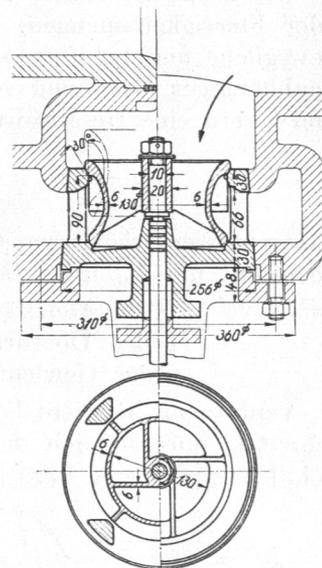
Doppelsitzauslaßventil am Niederdruckzylinder der Maschine Tafel I. M. 1:10.
